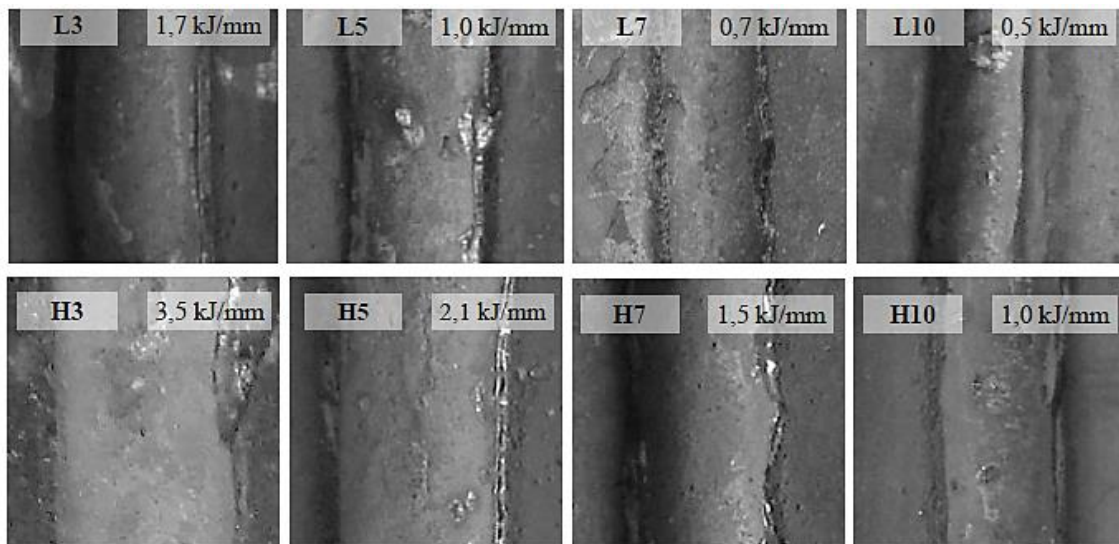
Vista superior de los cordones bead on plate. Soldados sin protección gaseosa.
